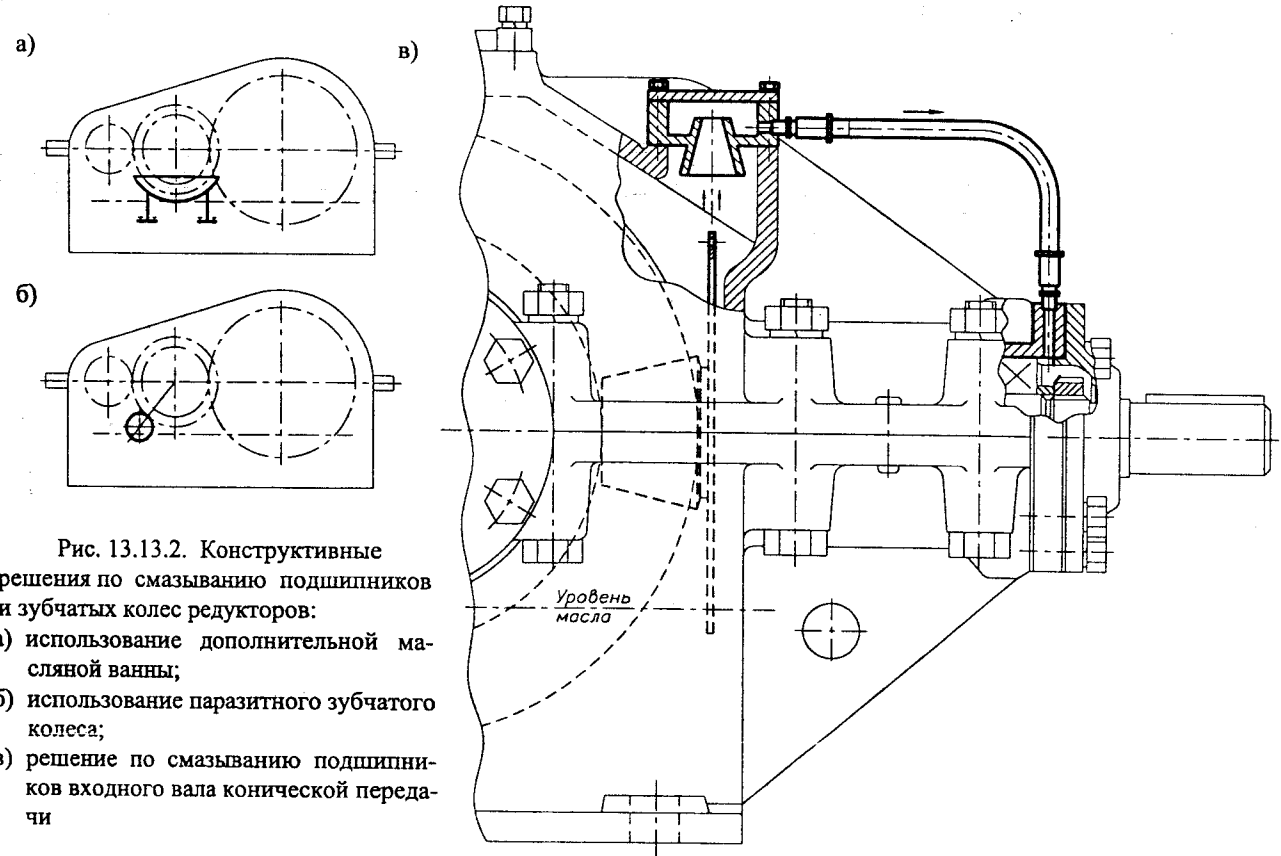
Конструктивные решения по смазыванию подшипников и зубчатых колес редукторов:
